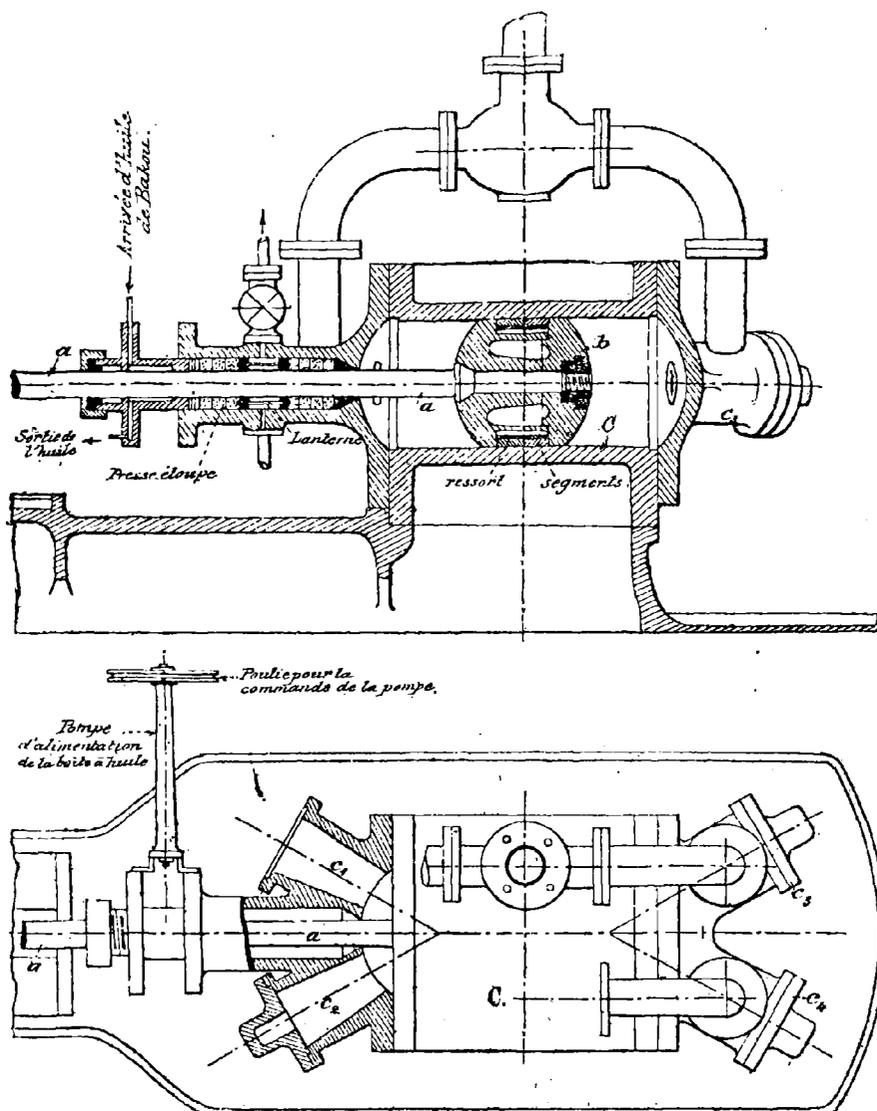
Compresseur de machine à ammoniac. Type Linde.
